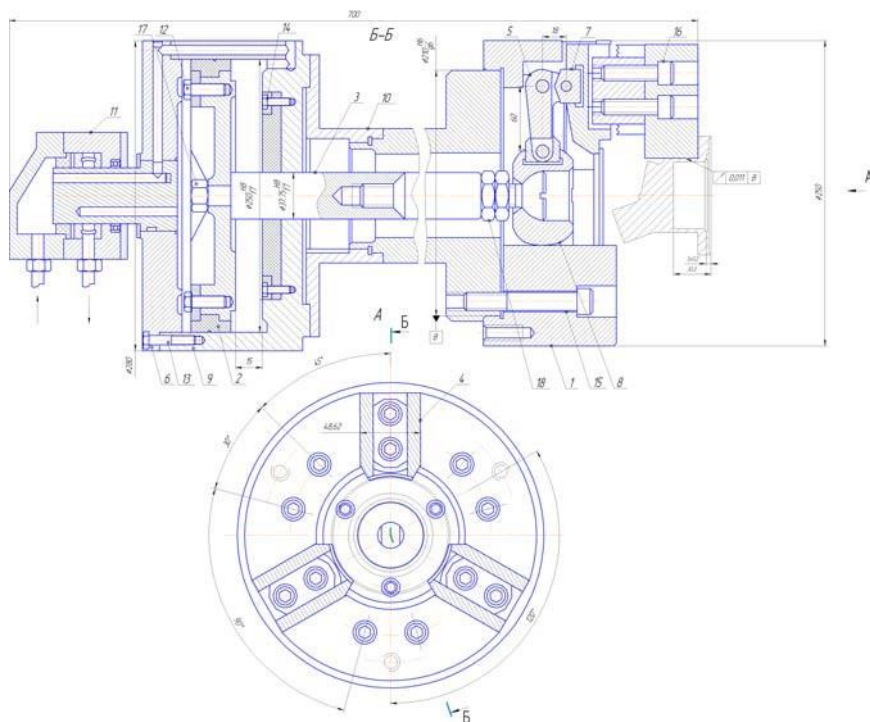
Общий вид приспособления для расточки Ø58H9 детали
